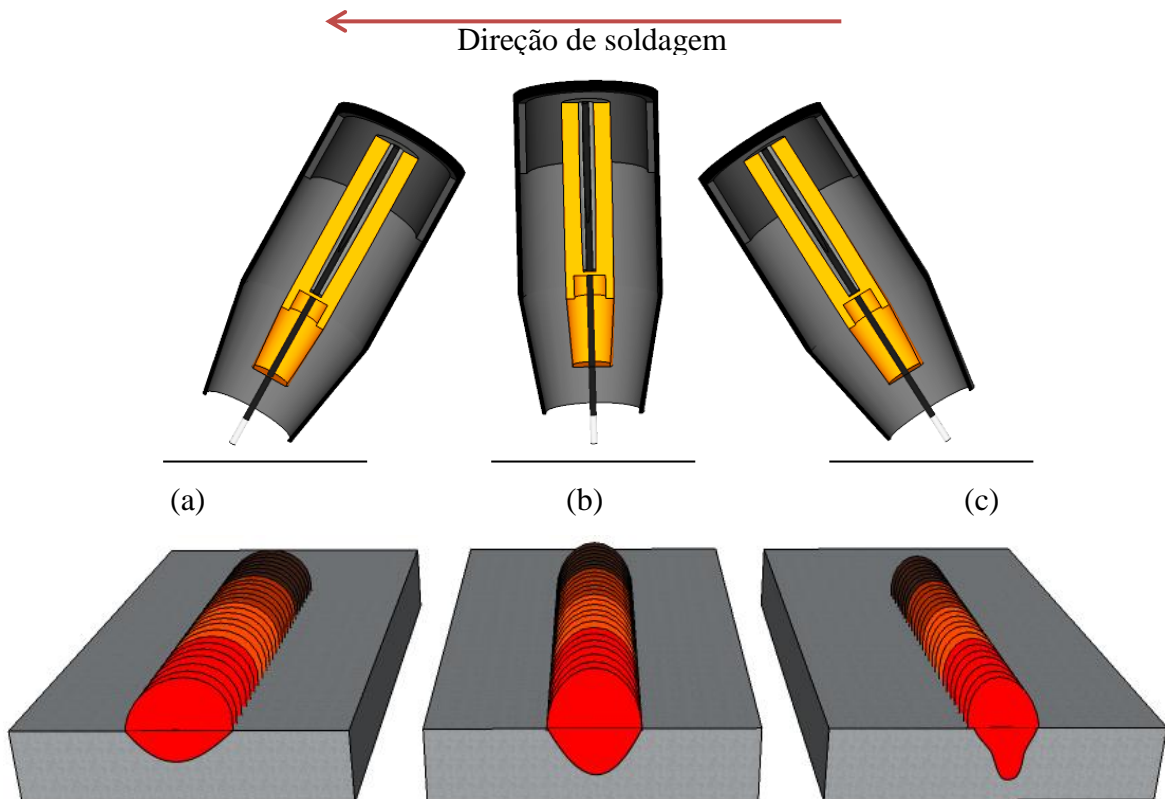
Efeito da posição do eléctrodo e a técnica de solda sobre o cordão (a) ângulo de empurre. (b) ângulo perpendicular (c) ângulo de arrastre.
